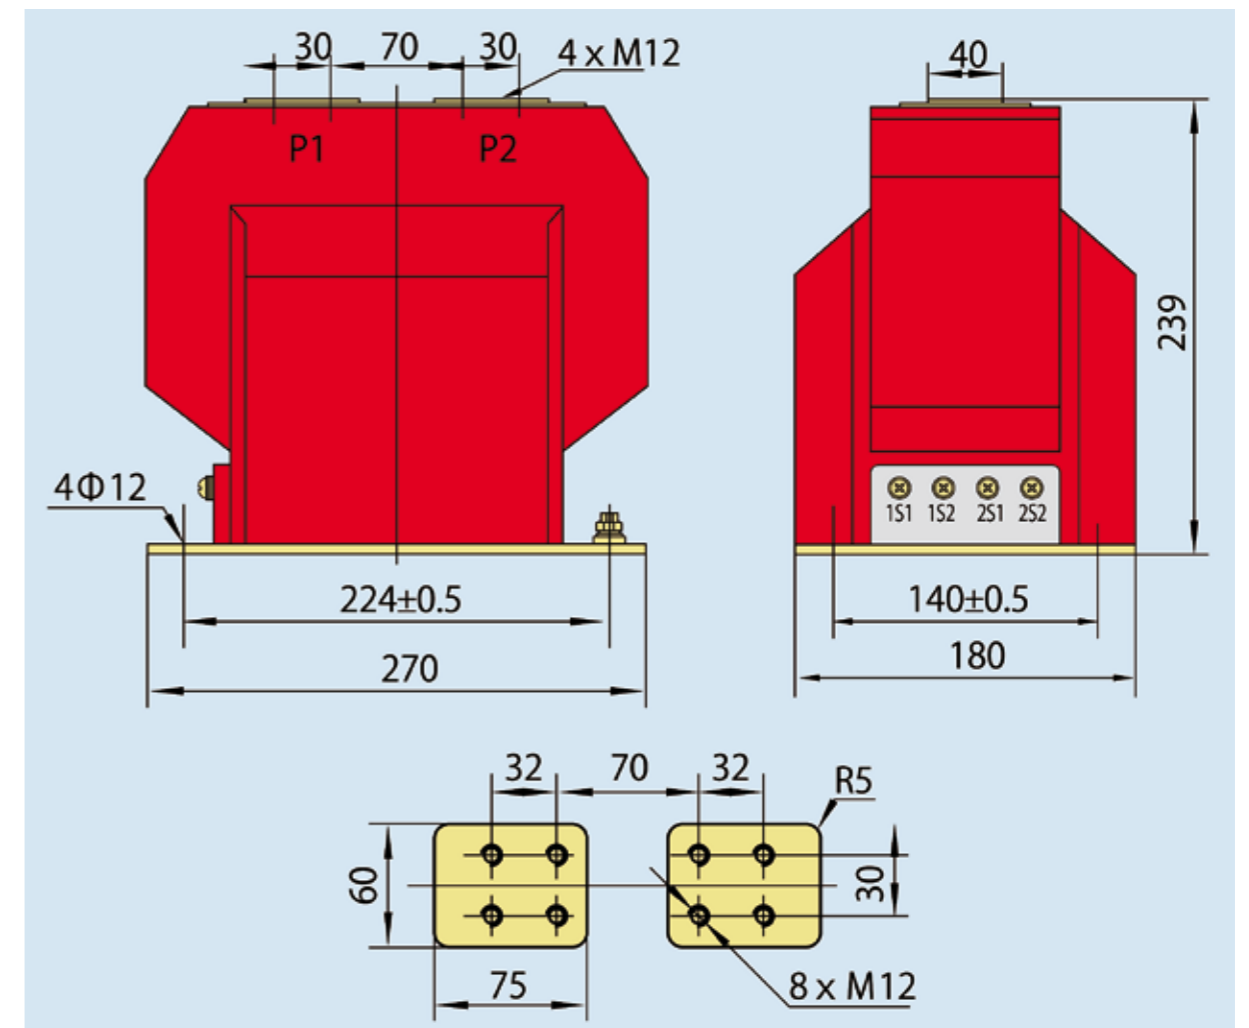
Внешний вид и размеры трансформатора тока LZZQB6-10
